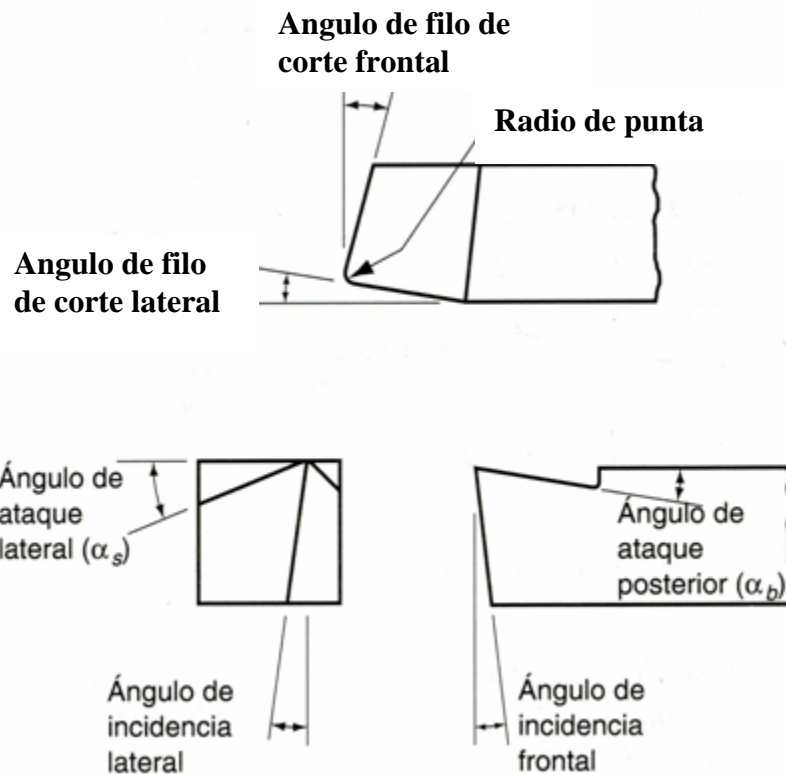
Elementos fundamentales de la geometría de una herramienta de corte (Groover, 1996)
